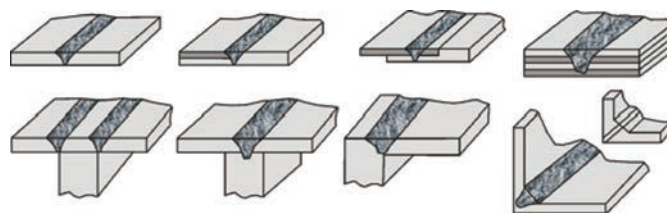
Сварные соединения, получаемые при СТП.
